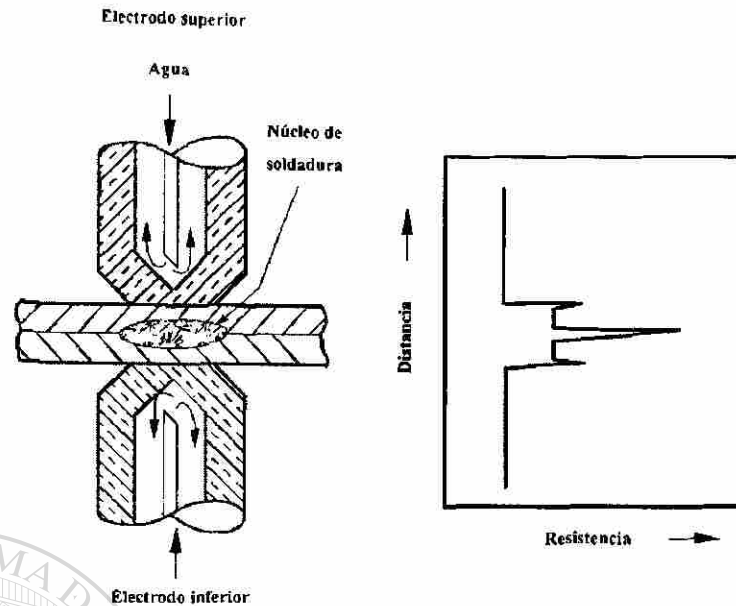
Esquema representativo de la soldadura por puntos ⁽³⁶⁾.
